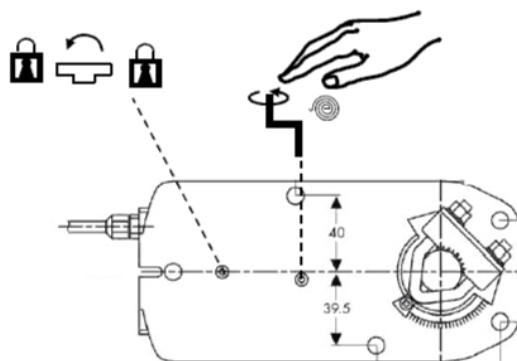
Ручное управление валом привода типоразмера NAFA 1(2)-08(S)
